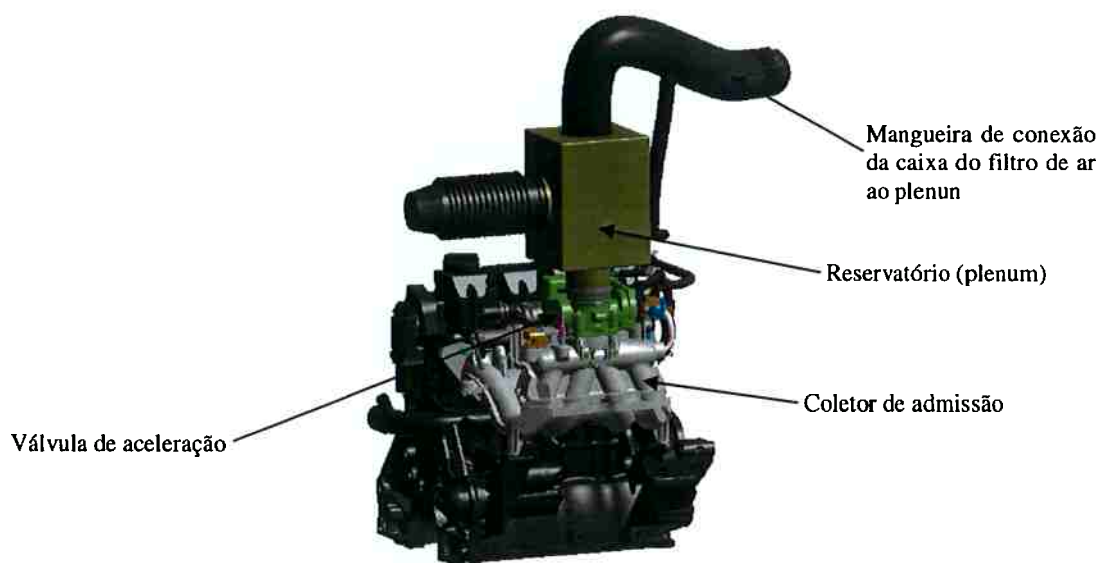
Sistema de admissão de ar do motor testado com válvula de aceleração montada na posição original e reservatório (plenum) montado na posição vertical com entrada da massa de ar filtrada pelo lado superior deste.
